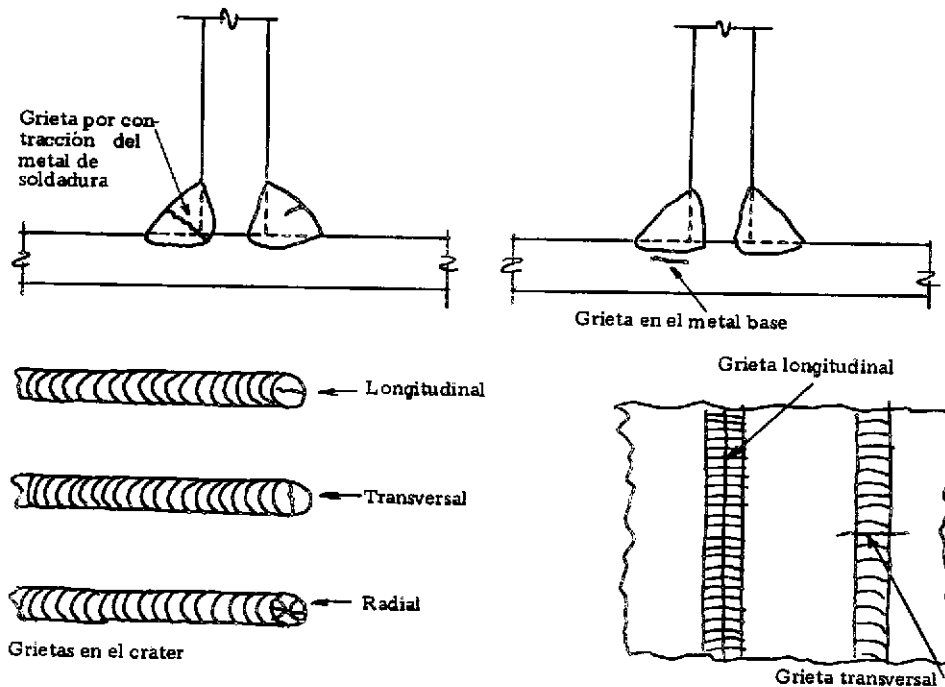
Tipos de grietas en el metal de soldadura.
